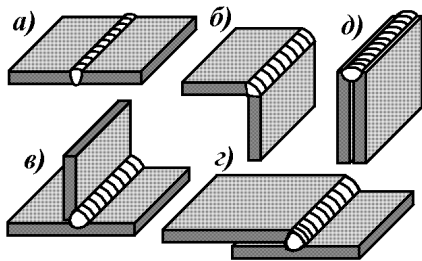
Типы сварных соединений: а) стыковое; б) угловое; в) тавровое; г) нахлесточное; д) торцовое
